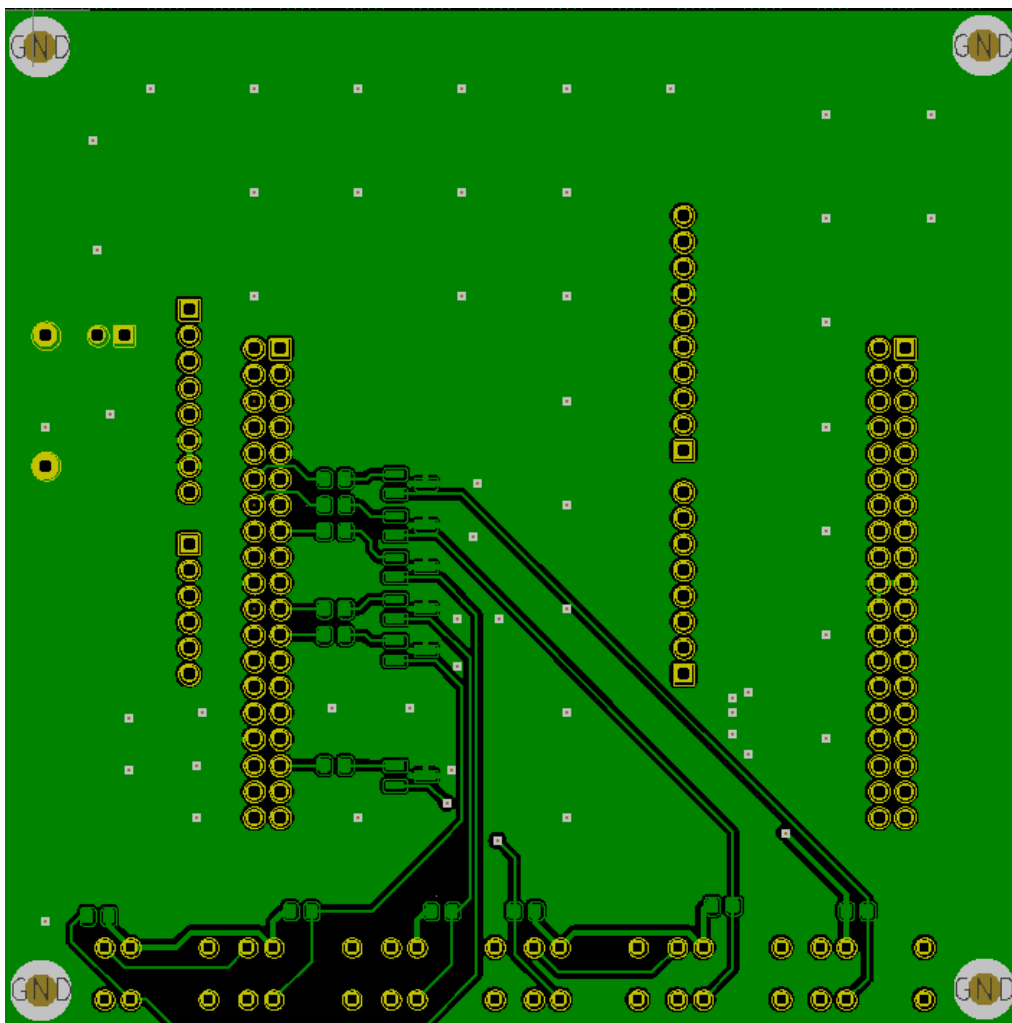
Schemat layoutu PCB łóżka testowego dla wariantu 1.
